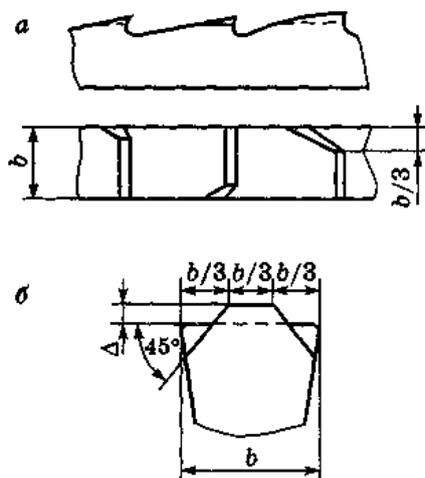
Схемы резания прорезными и отрезными фрезами
